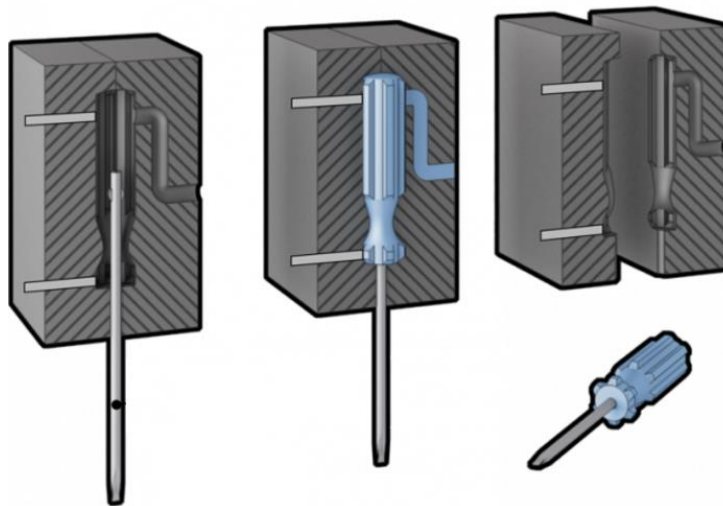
Colocação do inserto no molde (adaptado de [7])
